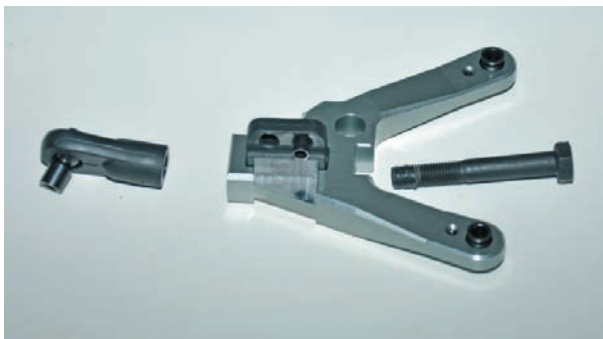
Kugelgelenkhalter, Stoßdämpferhalterung und Sechskantschraube des alten Querlenkers sind in den neuen aus Aluminium einzubauen.
